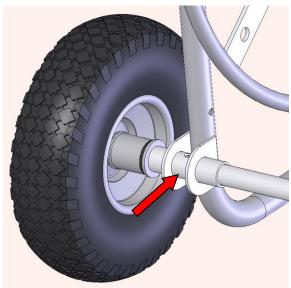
Radachsenbefestigung 3-teilig aussen am Rahmen angeschweisst. Radachsenfixierung mittels einem Schwerspannstift.
